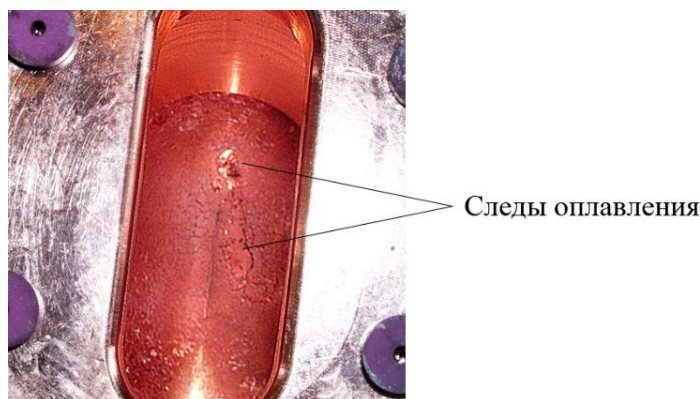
Фото внутренней поверхности базовой конструкции коллектора с оплавлением конусообразной поверхности.
